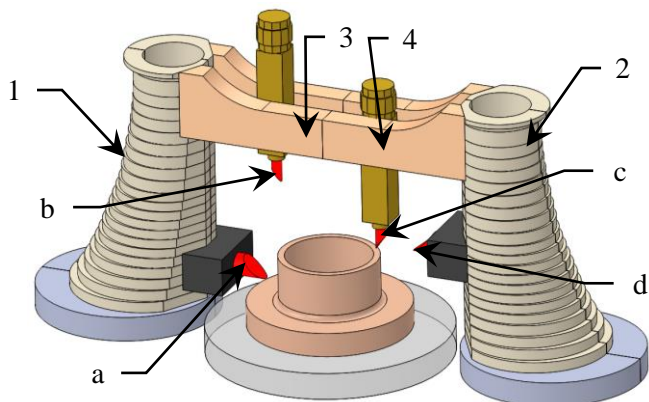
Компоновка станка с порталом из двух бионических башен (1, 2) и траверсы (3, 4): a, d – инструменты суппортов; b, c – инструменты ползунов
